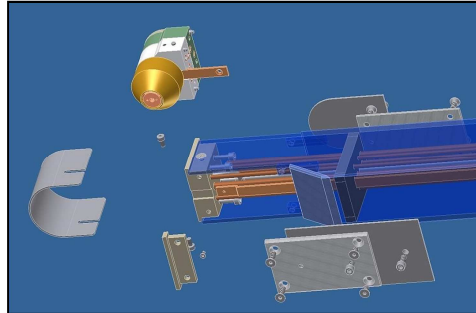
Tocha modelo HPI 350 de soldagem PTA do fabricante Kennametal.
